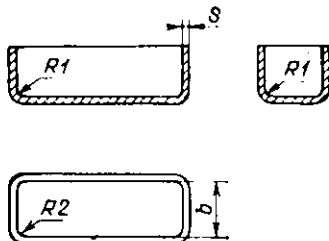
Радиусы сопряжения стенок прямоугольной детали
